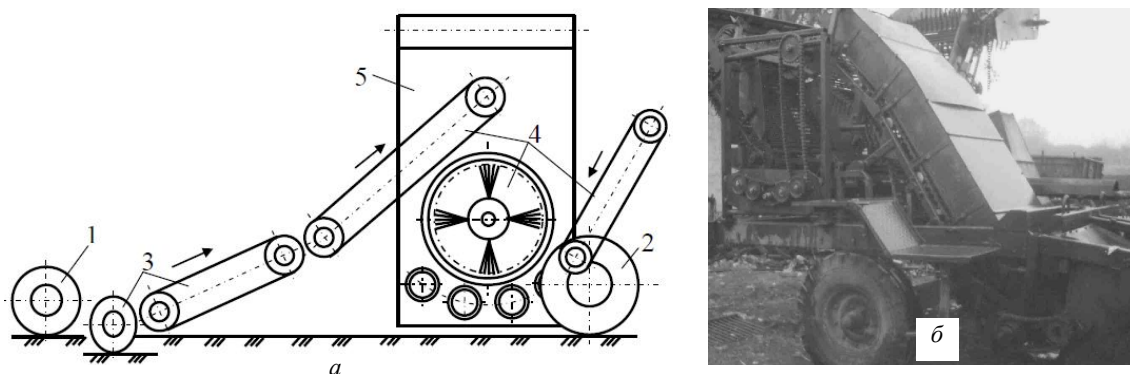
Конструктивна схема (а) та загальний вигляд (б) модернізованої коренезбиральної машини: 1, 2 – копіювальне та опорне колесо; 3 – однодисковий сферичний копач з приймальним транспортером; 4 – ТОС; 5 – завантажувальний транспортер
